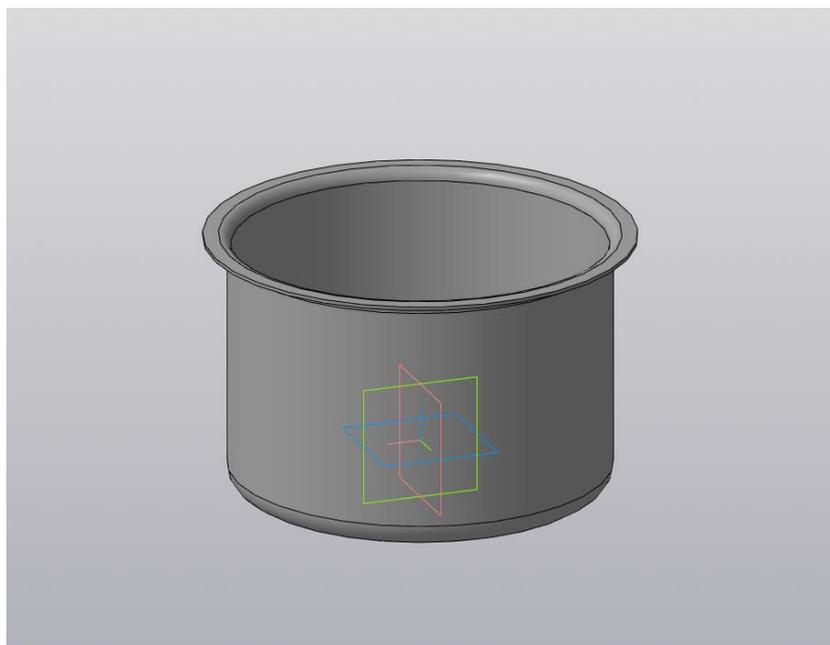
3D модель детали «Корпус кастрюли»
